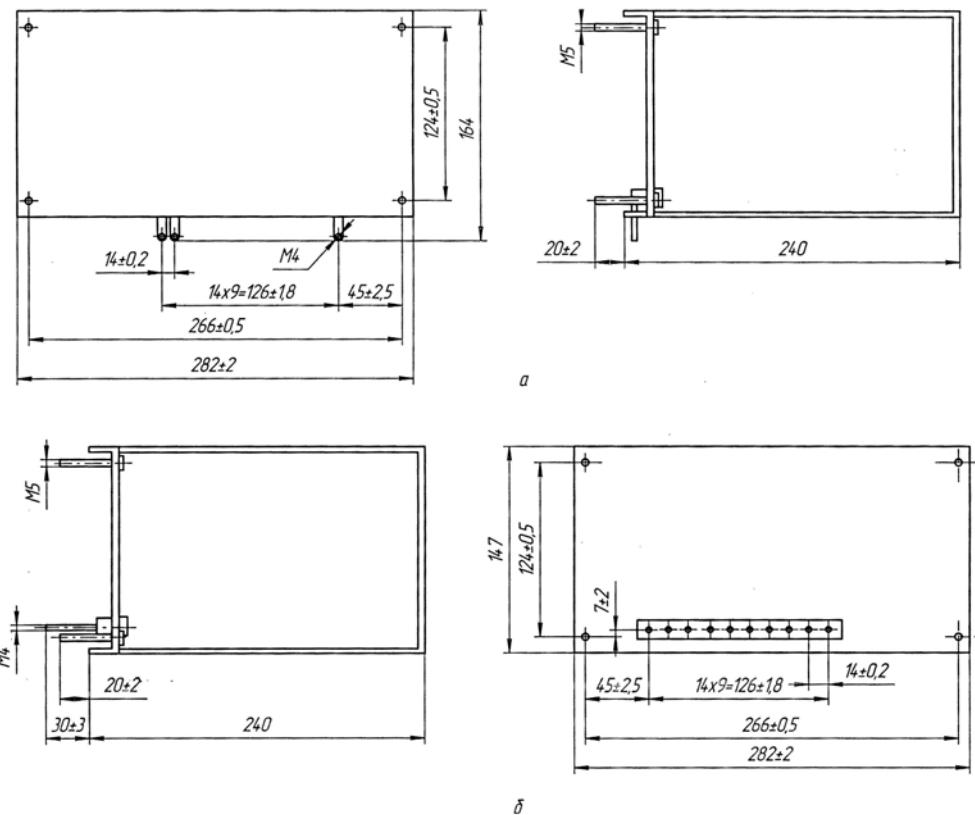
Габаритные, установочные и присоединительные размеры блоков БПЗ-400.
